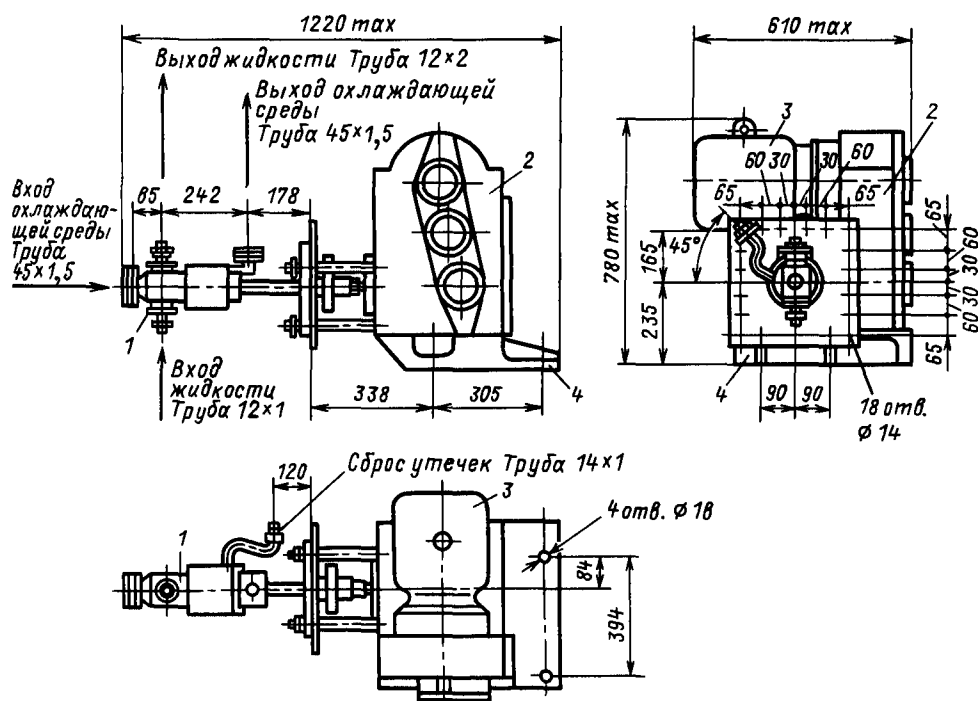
Габаритный чертеж насоса 21НСГ-25/20А-Л:
